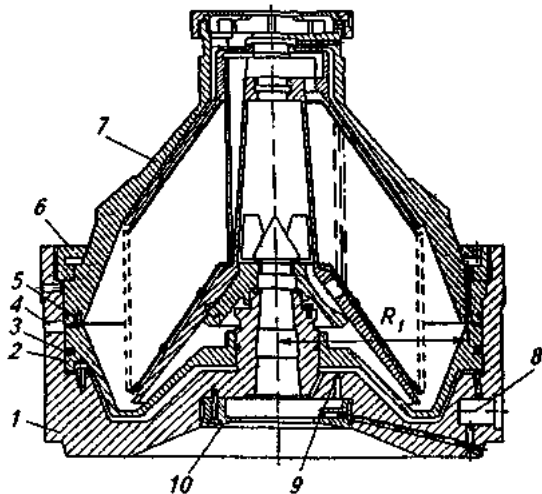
Барабан сепаратора-сливкоотделителя с периодической выгрузкой осадка: 1 - основание барабана; 2 - подвижное днище; 3,5 - уплотнительные кольца; 4 - окно для выгрузки осадка; 6 - затяжное кольцо; 7 - крышка барабана; 8 - клапан разгрузки; 9 - жиклер; 10 - распределительное кольцо буферной воды
